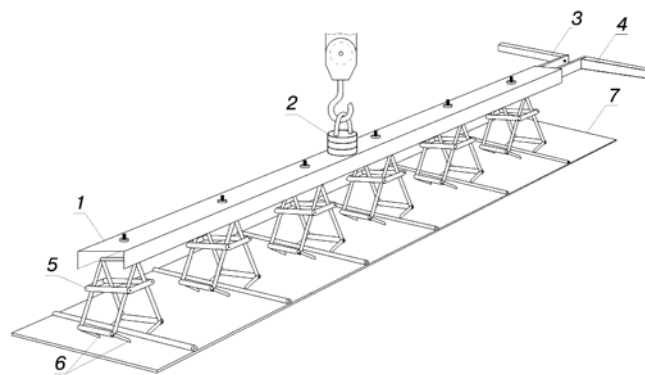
Принципиальная схема траверсы с захватывающими механизмами для укладки декоративных ковров в форму: 1 – траверса с установленными на ней захватывающими механизмами; 2 – устройство принудительного снижения; 3 – рычаг управления захватами; 4 – рычаг управления устройством принудительного снижения; 5 – замыкающая рама; 6 – зажимы устройства захвата; 7 – декоративный ковер с установленными анкерами
